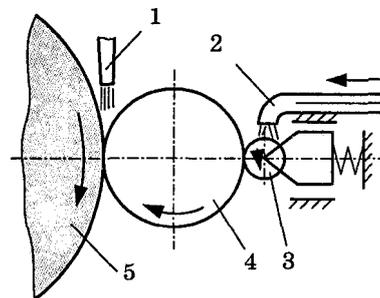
Схема подачи СОТС свободно падающей струей при одновременной контактной смазке заготовки:
